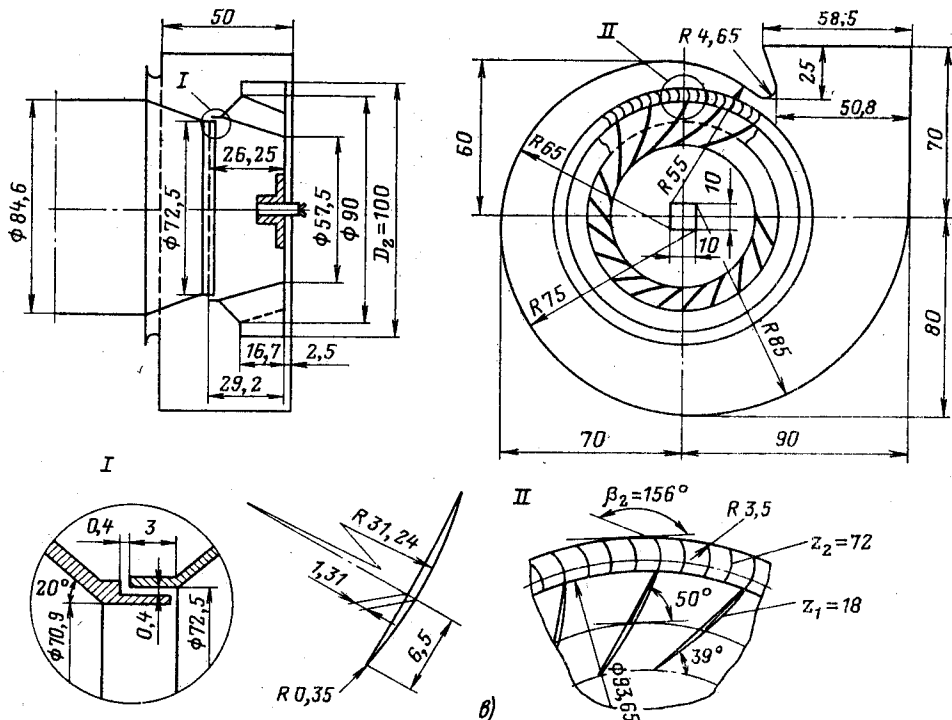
Аэродинамические схемы центробежных вентиляторов:
